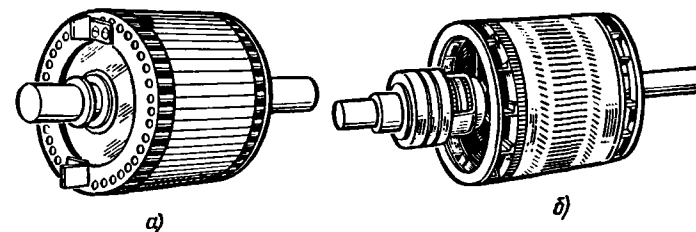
Общий вид ротора асинхронного двигателя с короткозамкнутой (а) и фазной (б) обмотками
